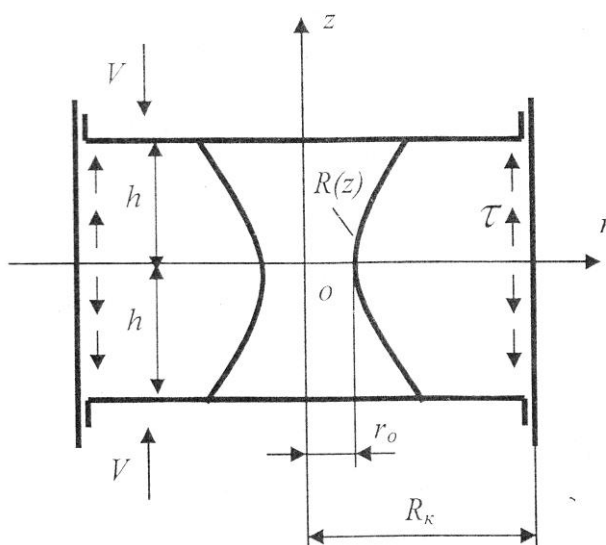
Схема осадки полый цилиндрической заготовки в пресс-форме
